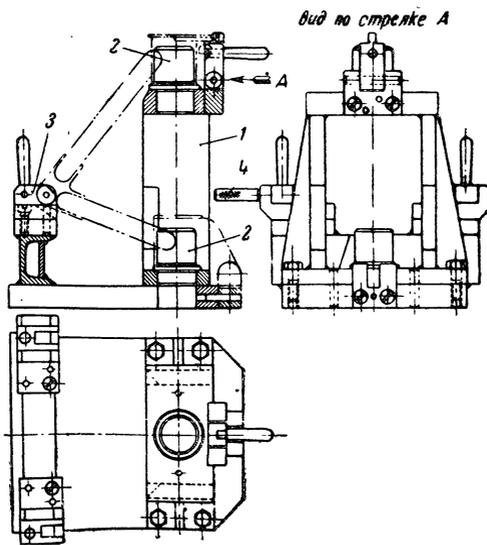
Приспособление для контроля сварного кронштейна.
